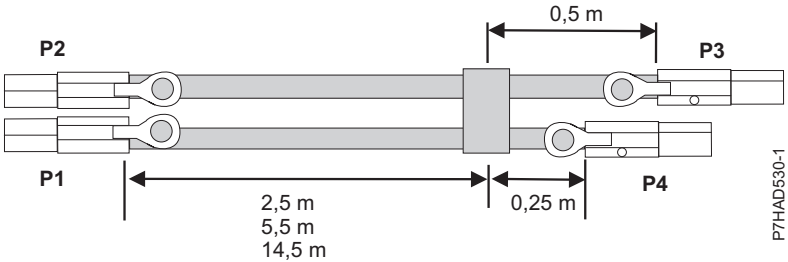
Longituds de cables de conjunt de cable X SAS extern
